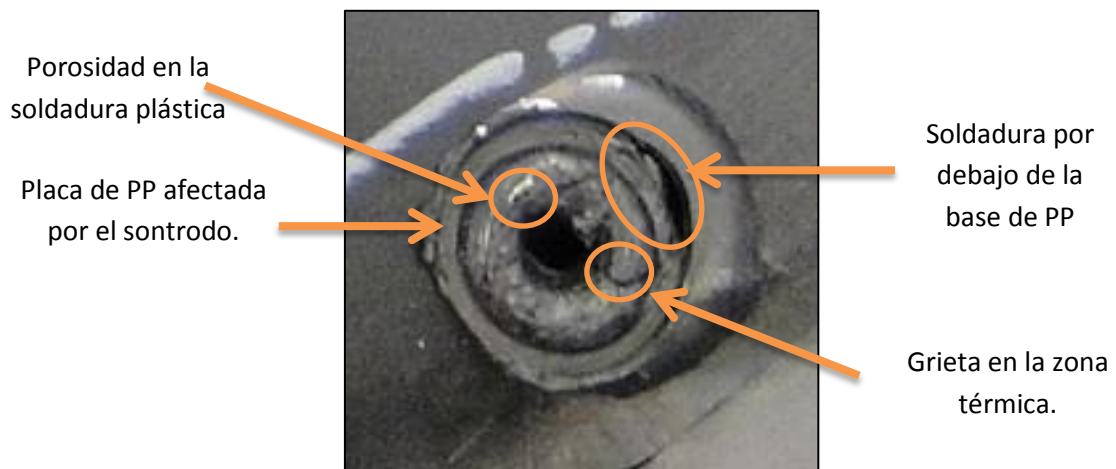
Soldadura circular con menor fuerza de desprendimiento.
